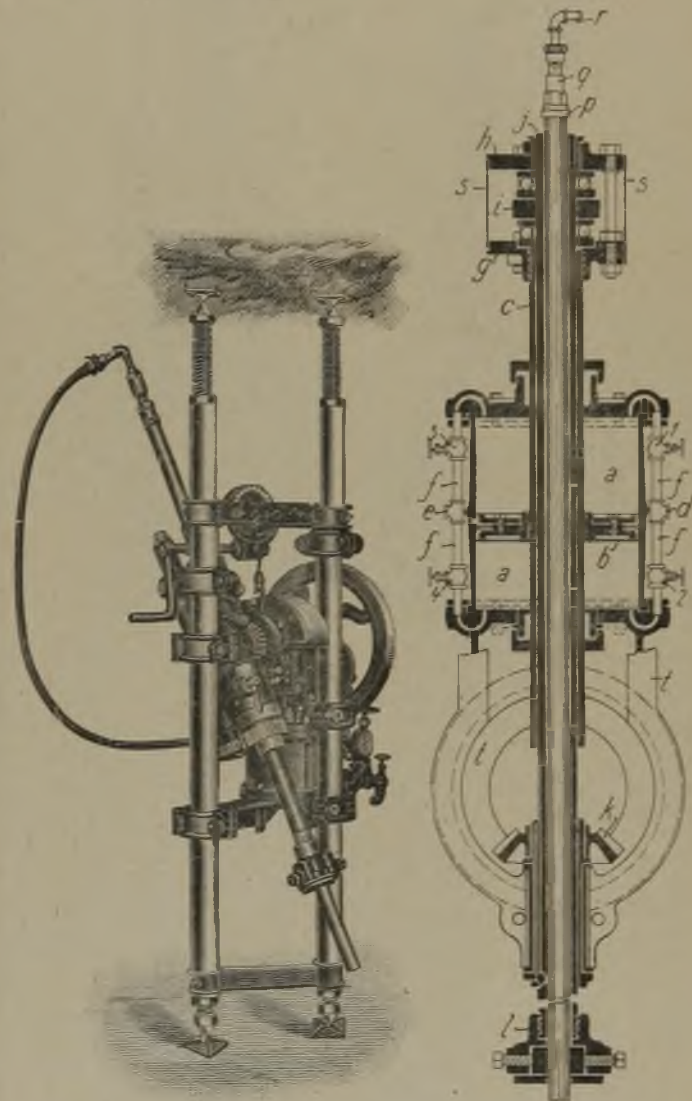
Schürfbohrmaschine für Preßluft- oder Dampftrieb mit Winde für die Einstellung des Bohraparates. Sullivan Machinery Co. Chicago.
